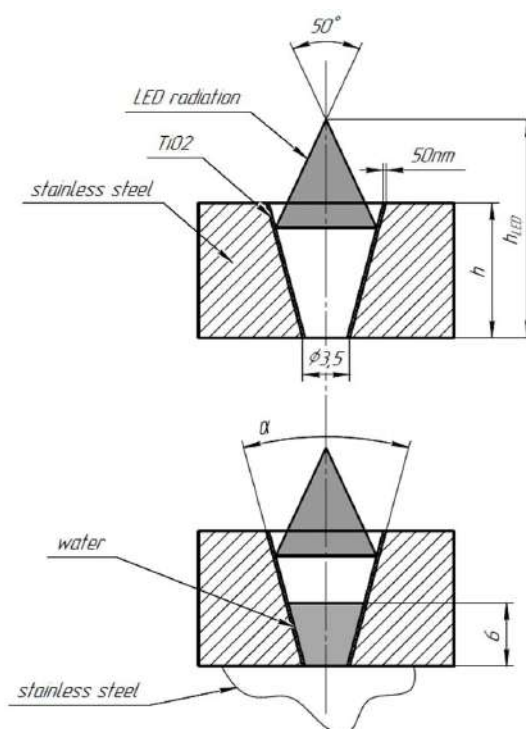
Чертеж лунки фотокаталитического микрореактора
